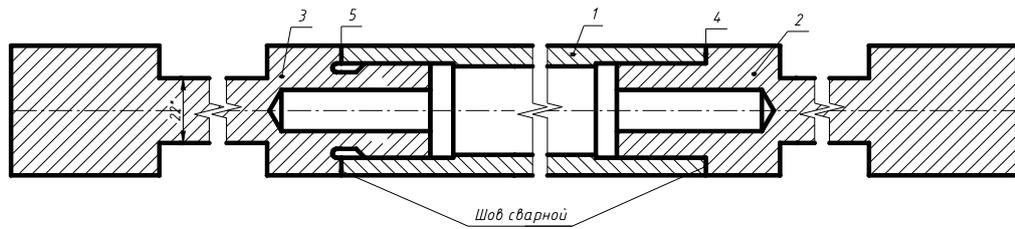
Образец трубы 45×5 с приварными элементами замка при нагревании за счет трения
